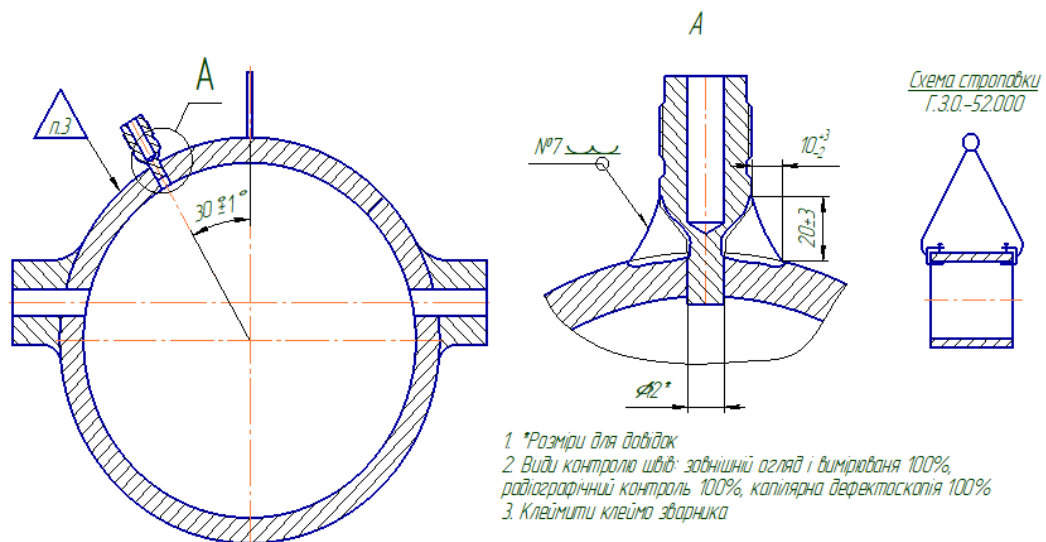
Ескіз приварювання штуцера до корпусу
